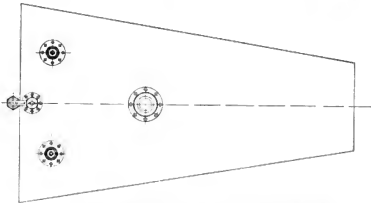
Explosionssicherer Benzintank der „Feg“ in Salzkotten.
